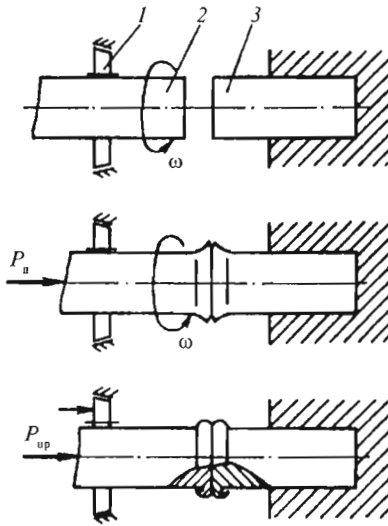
Схема сварки трением с непрерывным перемешиванием:
